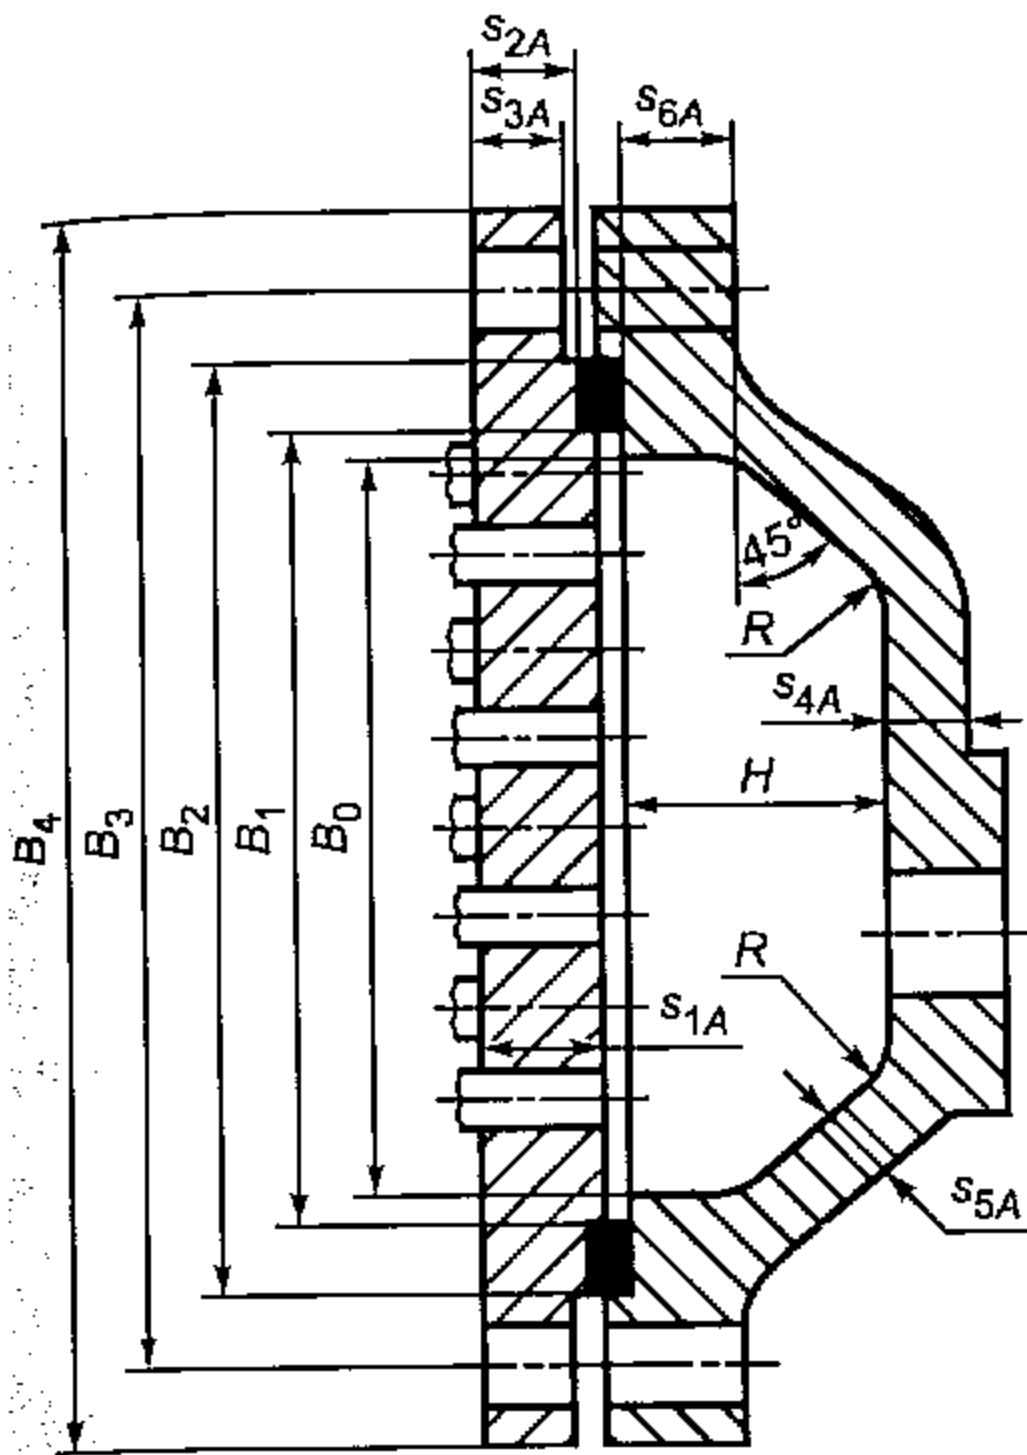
Камера разъемной конструкции с литой или штампованной крышкой
